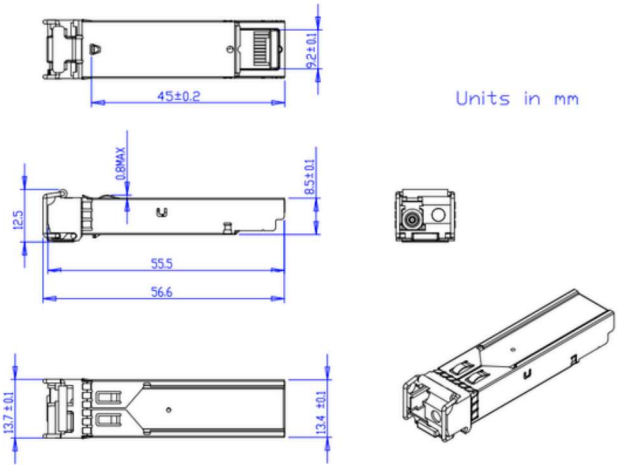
Desenho Técnico e Dimensões Mecânicas (em milímetros)
